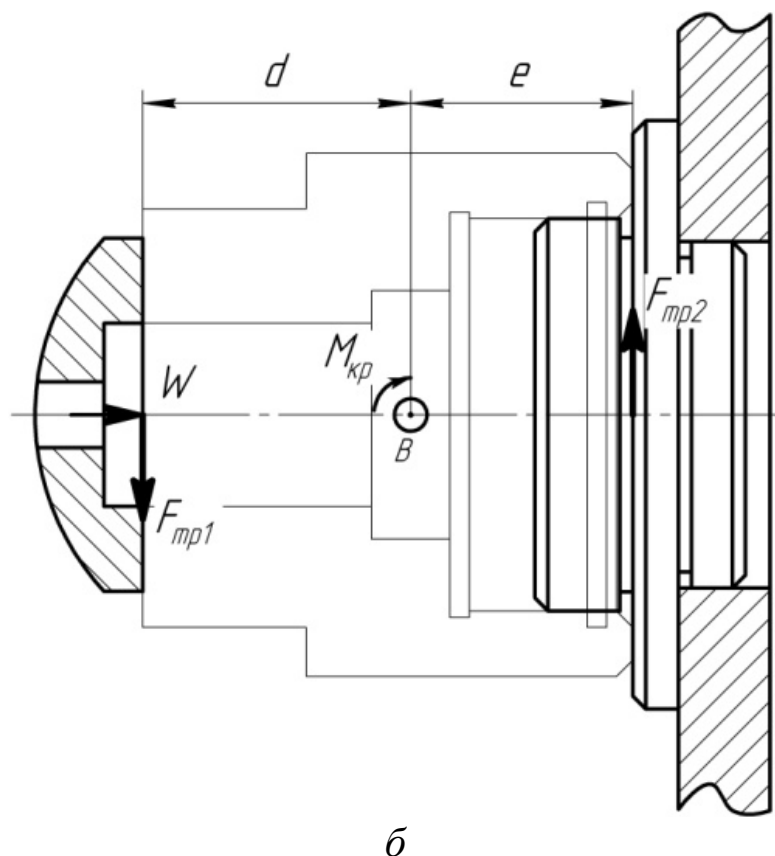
Расчётная схема для определения силы зажима заготовки
